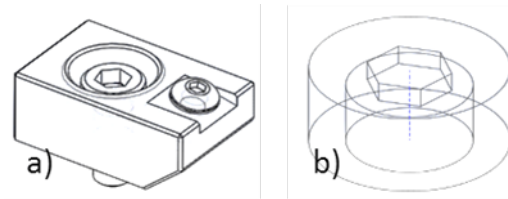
Sujetador vista isométricas cuerpo de alambre.
